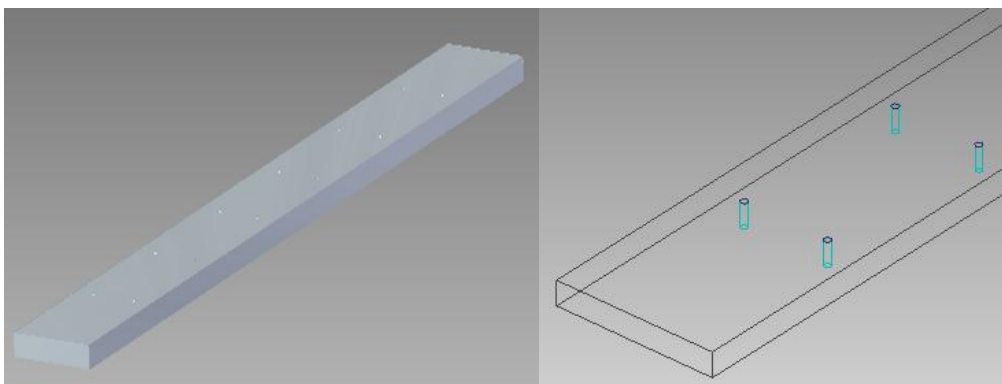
Placa removible diseñado mediante Solid Edge® ST5. Fuente propia.
